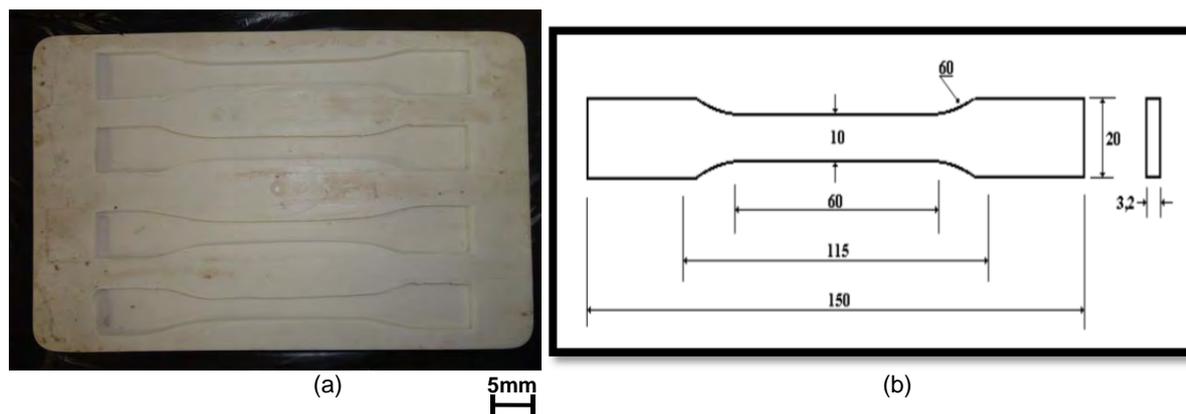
(a) Molde de silicone; (b) Dimensões (em mm) dos corpos de prova para ensaio de tração.
